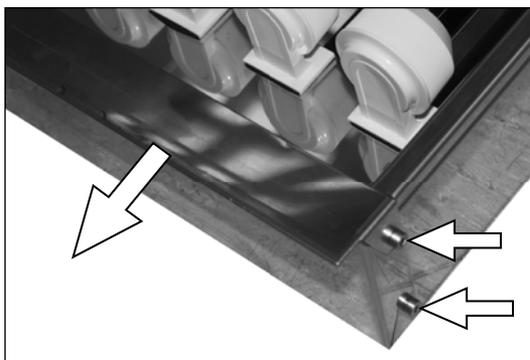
Innensechskantschrauben entfernen, Halteblech entfernen und Glasplatte herausnehmen
